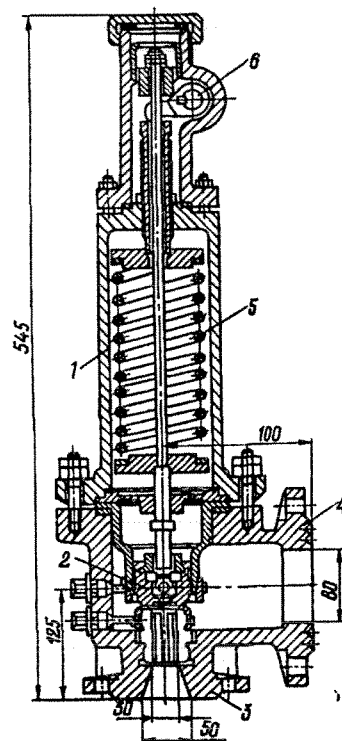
Предохранительный пружинный клапан типа ППК-4-50-16:
